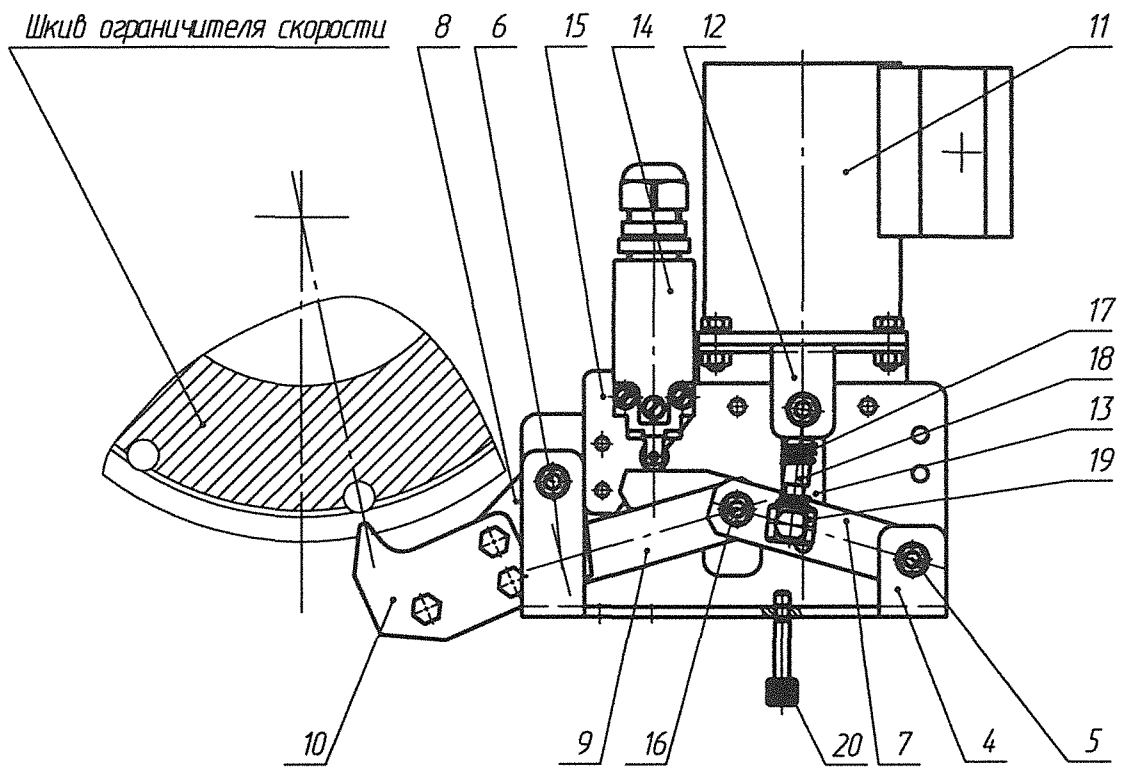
Общий вид устройства стопорного УС1020.07.00.000
